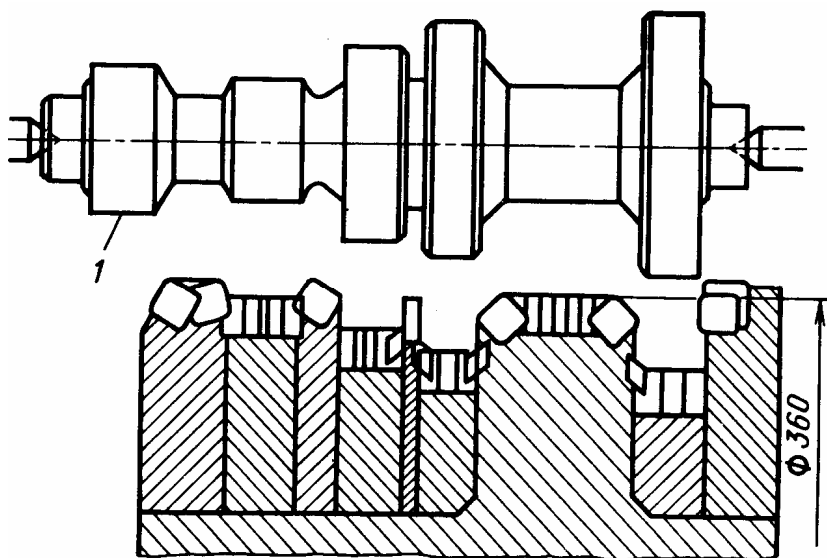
Схема контурного фрезерування заготовки деталі типу «східчастий вал» набором фрез фірми „Хейнляйнзйтц-ман” (ФРН); 1 – заготовка
